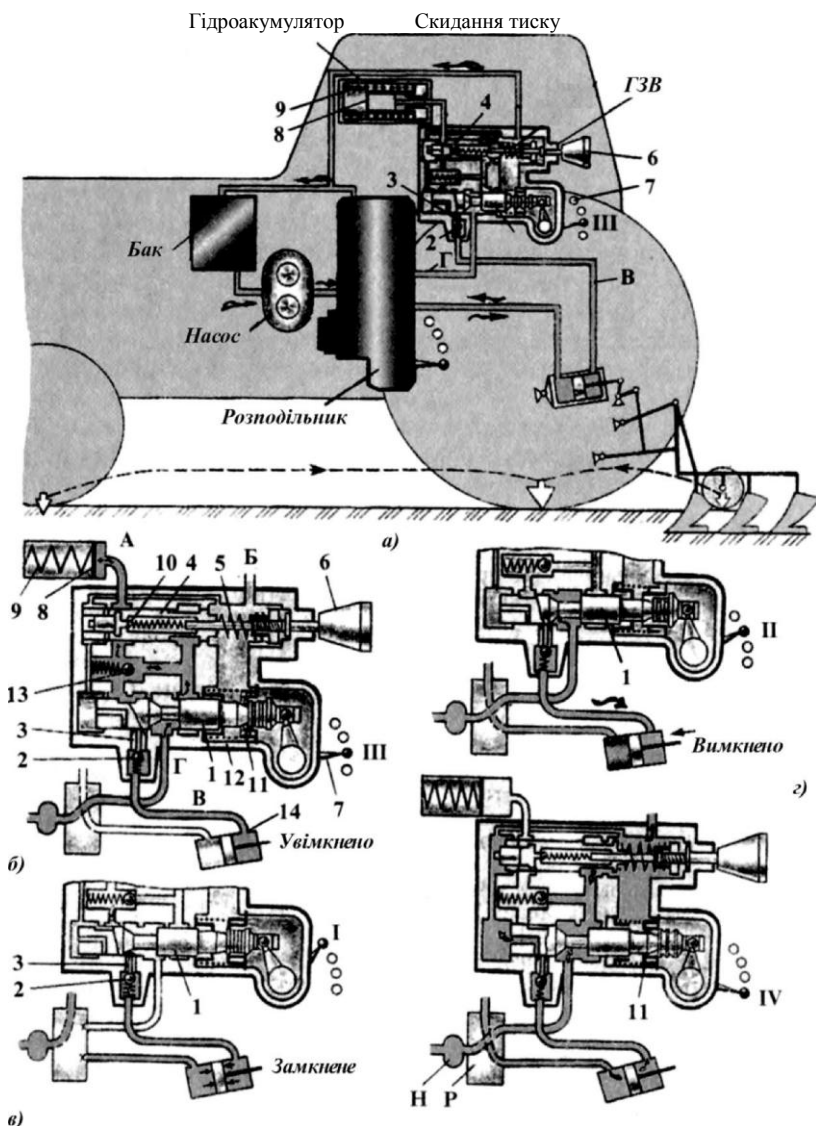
Схема роботи гідравлічного довантажувача ведучих коліс (МТЗ-80): а, б - ДВК увімкнений; в - ДВК вимкнений; г - ДВК замкнений; д - скид тиску; 1 - повзун; 2 - запірний клапан; 3 - штовхач; 4 - золотник; 5 - пружина золотника; 6 - маховичок; 7 - важіль керування повзуном; 8 - гідроаккумулятор; 9 - пружина гідроаккумулятора; 10 - запобіжний клапан; 11 - фіксатор; 12 - корпус; 13 - зворотний клапан; 14 - гідроциліндр; А, Б, В, Г - трубопроводи; Н - насос; Р - розподільник.
